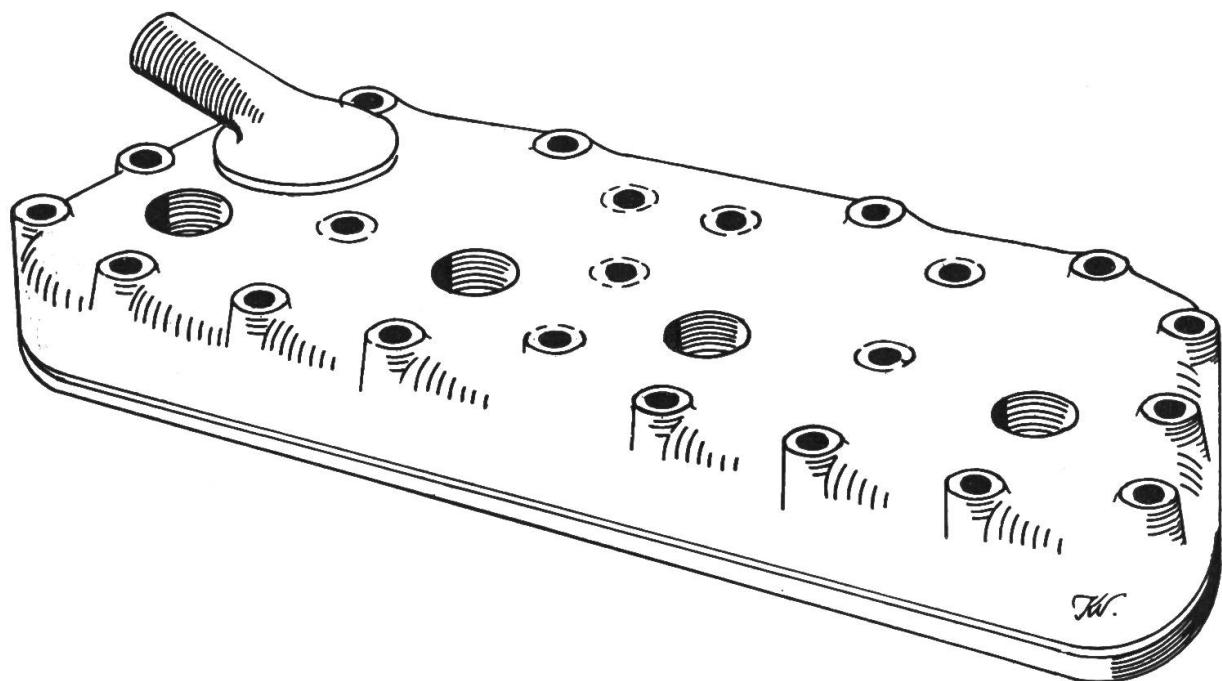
Zylinderkopf eines wassergekühlten 4-Zylindermotors.
